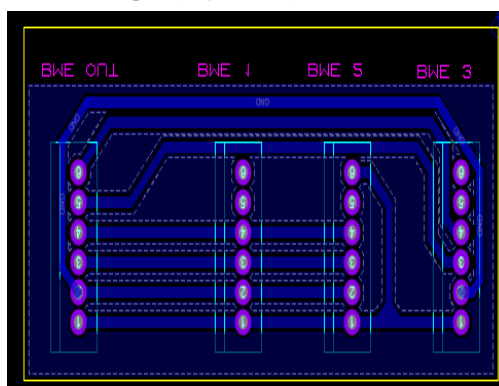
Vista de capas (Layer View) Placa PCB sensores BME280
